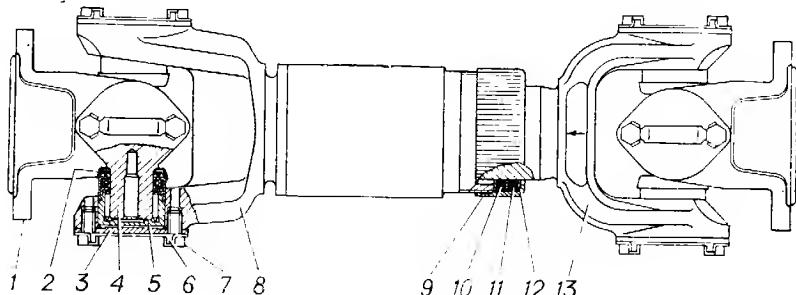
Карданный вал привода колесного редуктора (вал третьего типа):
